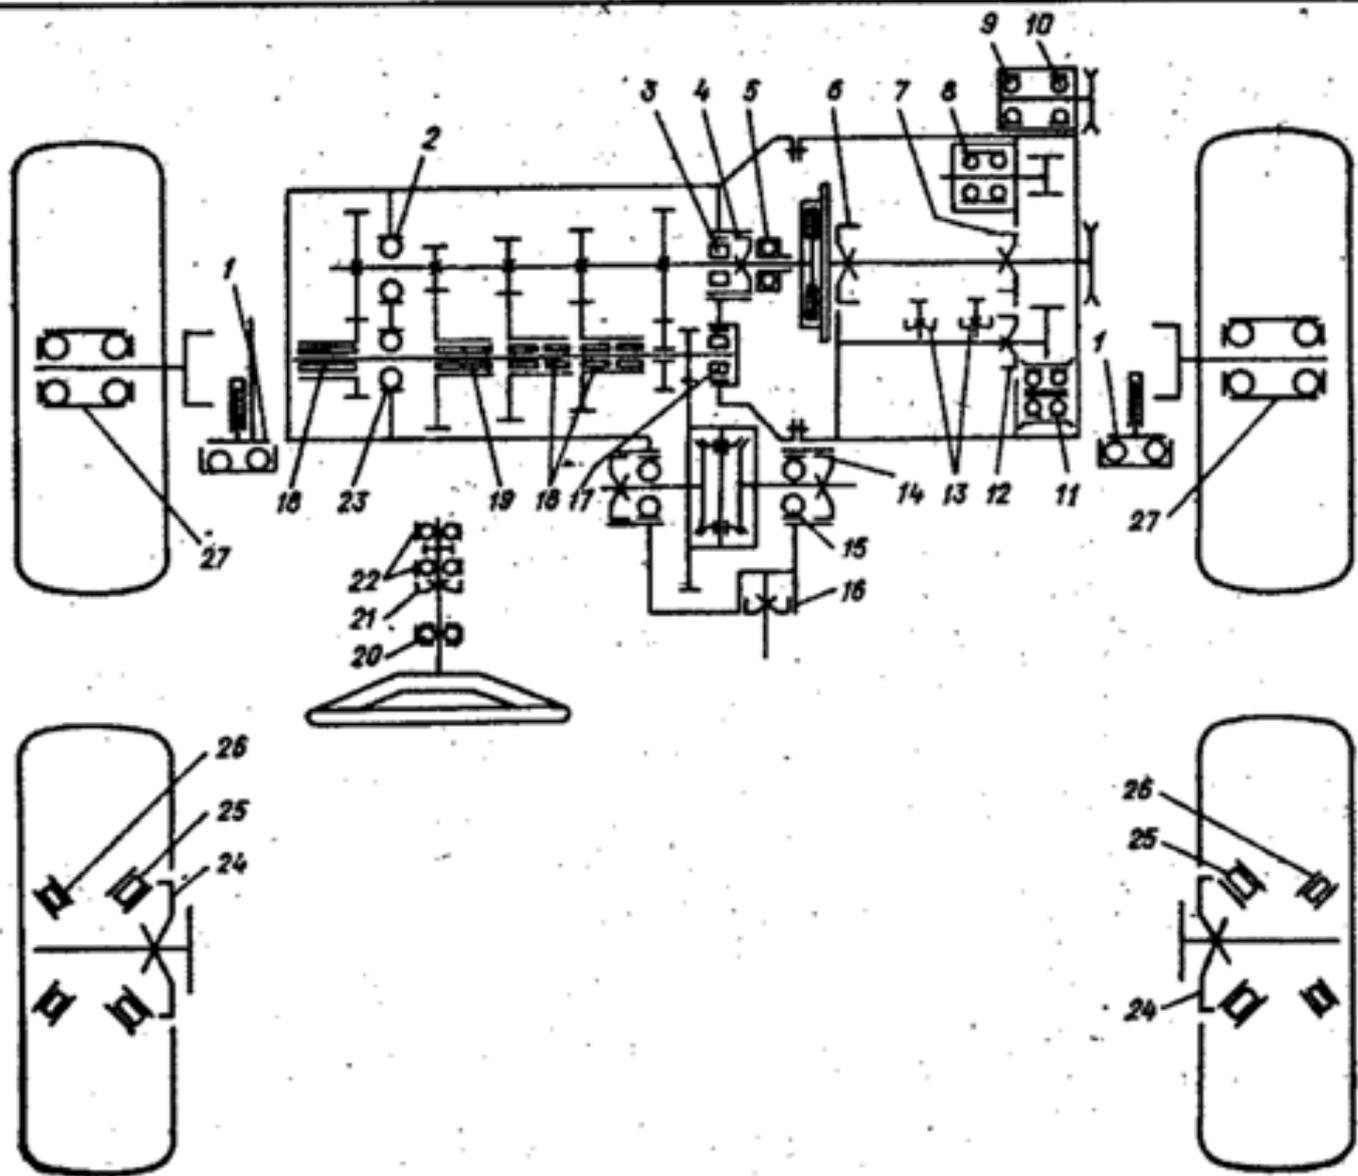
Схема расположения подшипников и уплотнительных манжет
